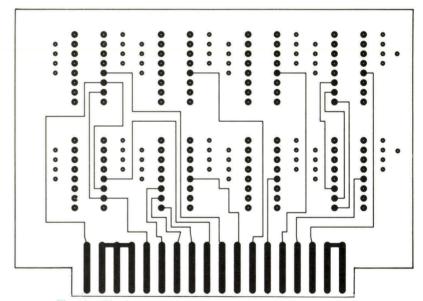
Circuit imprimé vu côté « soudures » d'une carte « fille »
